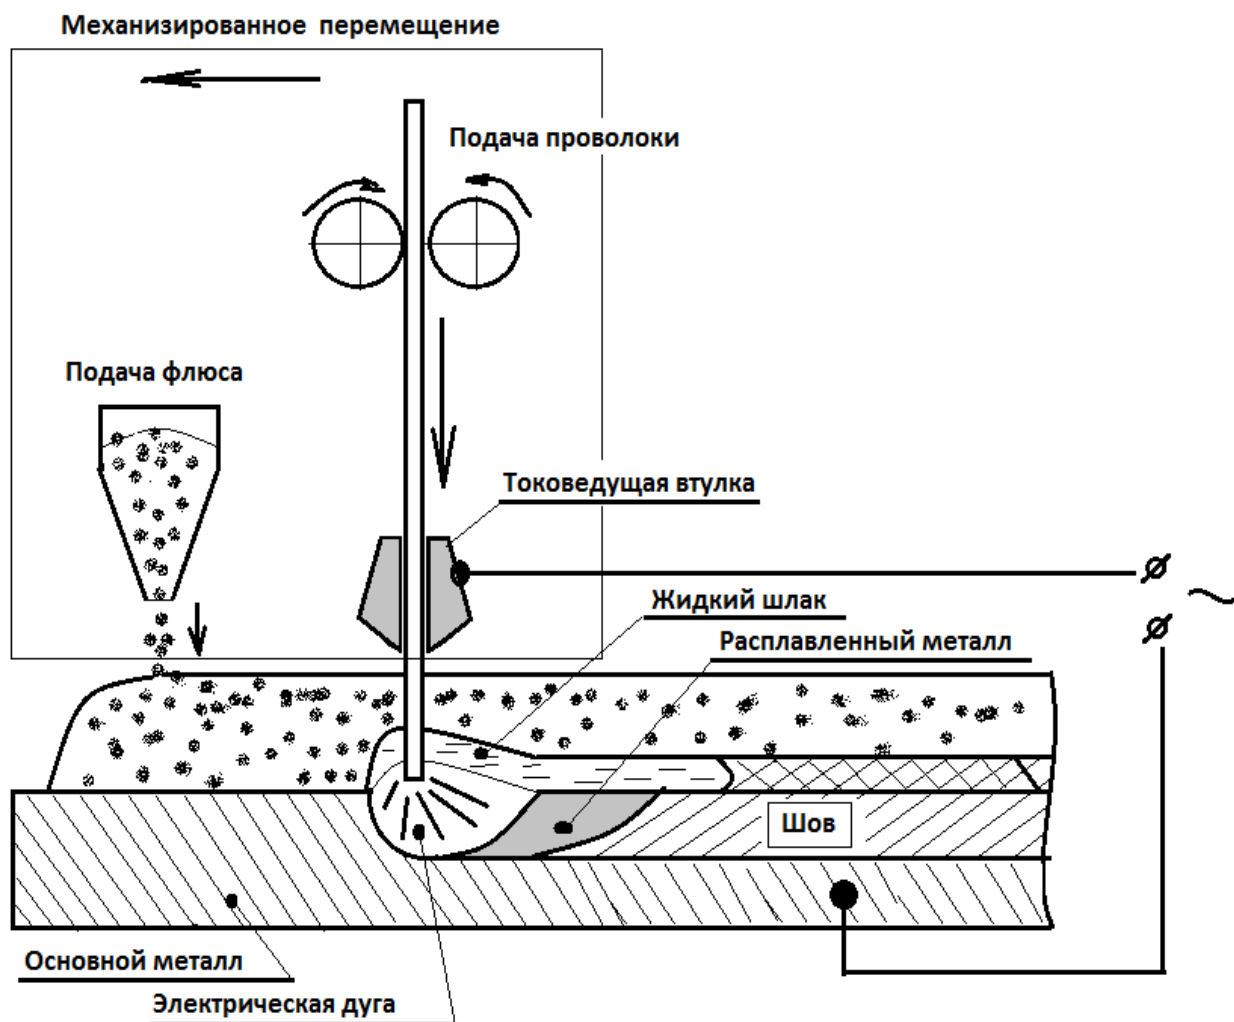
Схема сварки, наплавки под слоем флюса
